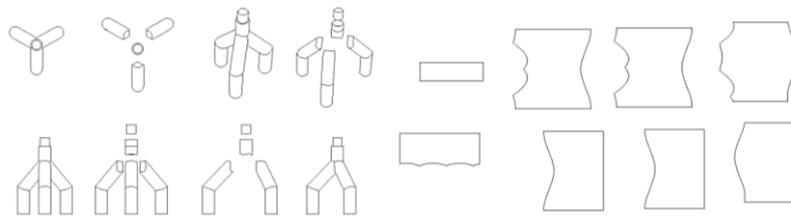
Piezas estructurales de unión y molduras para su fabricación.
